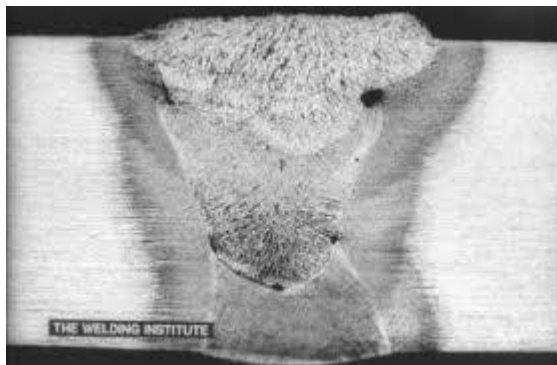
Рентгенограма зварного шва з внутрішніми дефектами
